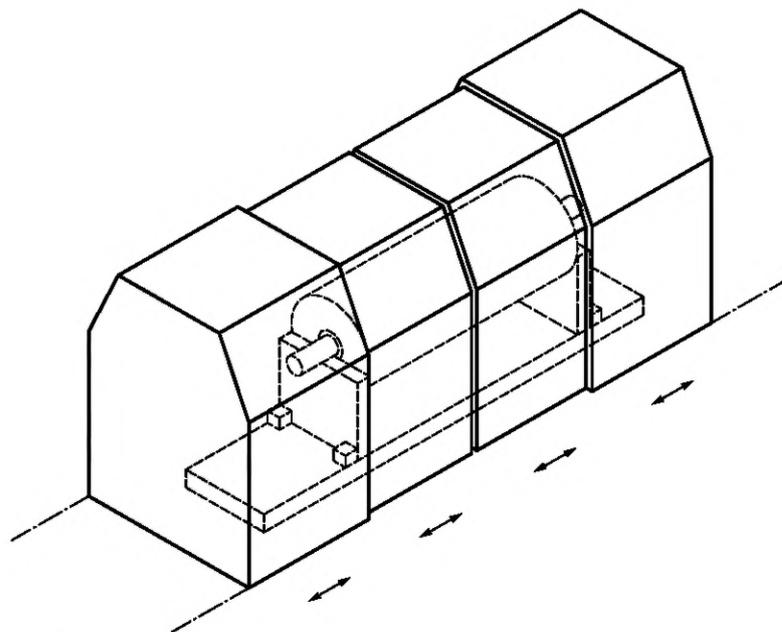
Телескопический кожух, полностью охватывающий балансировочный станок (класс защиты С)
